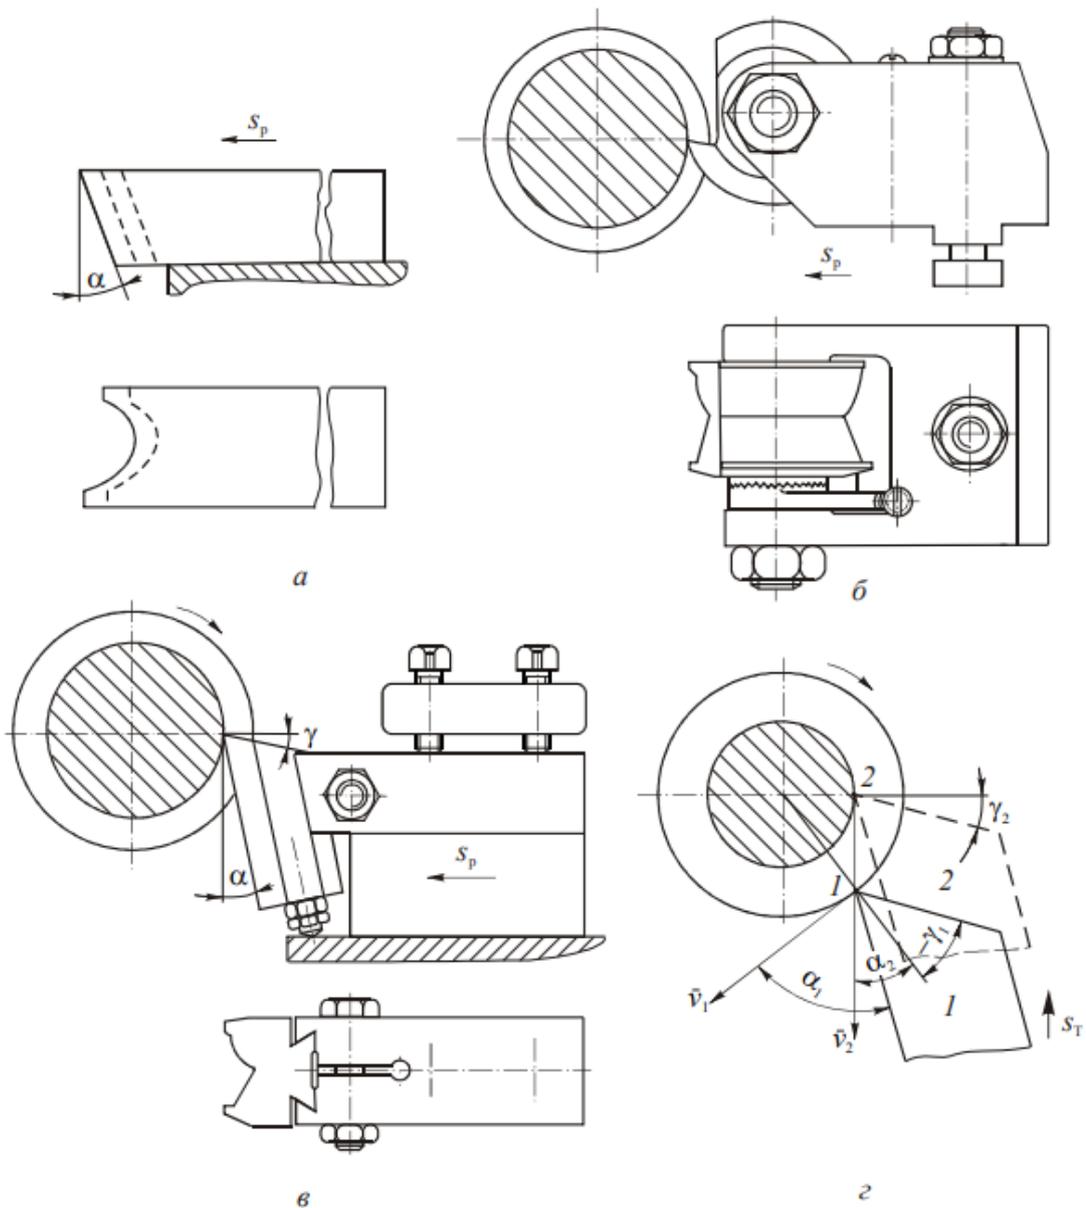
Типы фасонных резцов: а – стержневой; б – круглый; в – призматический радиальный; г – призматический тангенциальный
